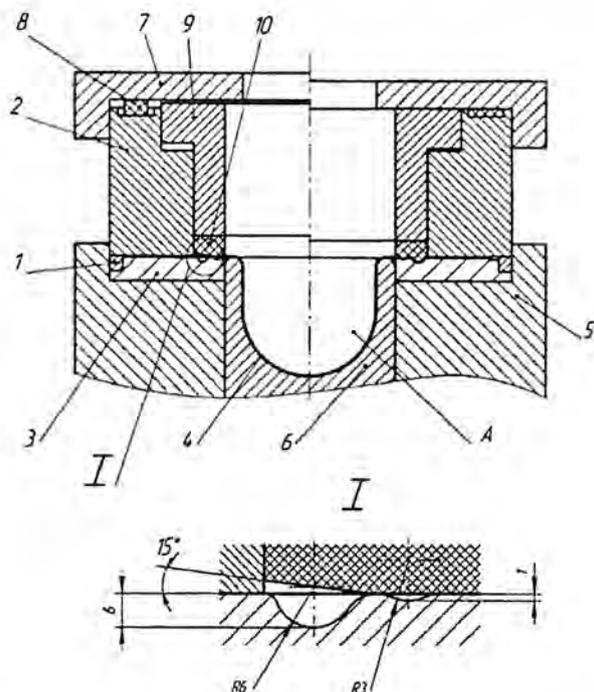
Технологическая оснастка для принудительной подачи вытягиваемого материала из периферии в очаг деформации с дополнительным резервированием материала заготовки в центре: 1 – кольцо; 2 – верхний прижим; 3 – нижний прижим; 4 – штампуемая заготовка; 5 – корпус устройства для дискретного перемещения пуансона; 6 – пуансон; 7 – крышка; 8 – резиновая (полиуретановая) прокладка; 9 – вкладыш; 10 – полиуретановое кольцо
